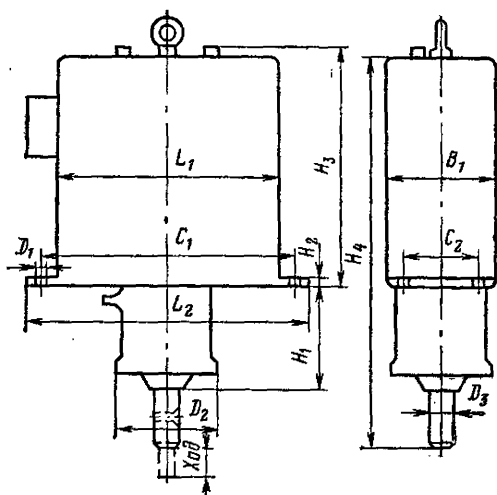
Массогабаритные размеры электромагнитов КМТ.
